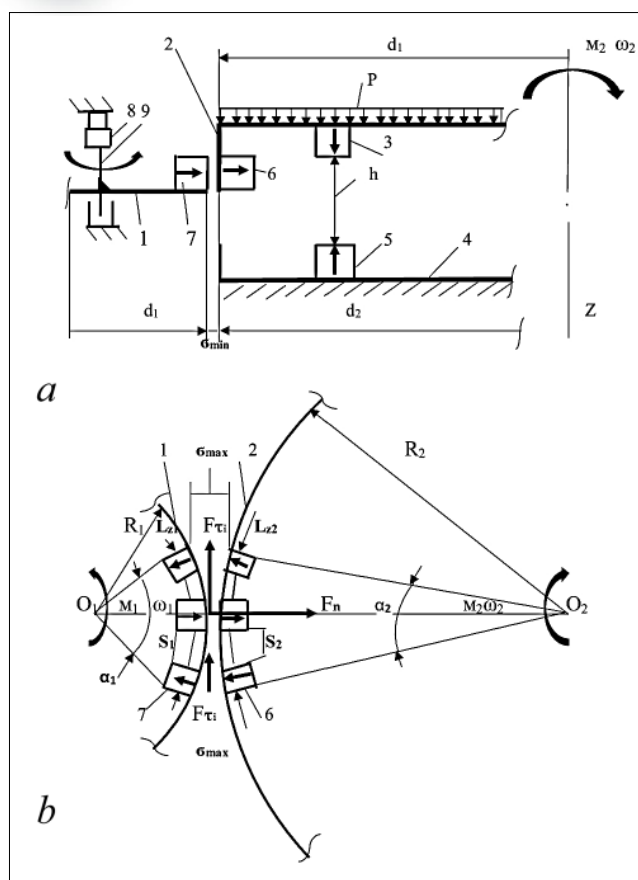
Схема магнитного подвеса и привода левитирующей платформы карусельного типа на основе цилиндрической магнитной передачи с внешним зацеплением: а – вид сбоку; б – вид сверху без магнитов левитации
